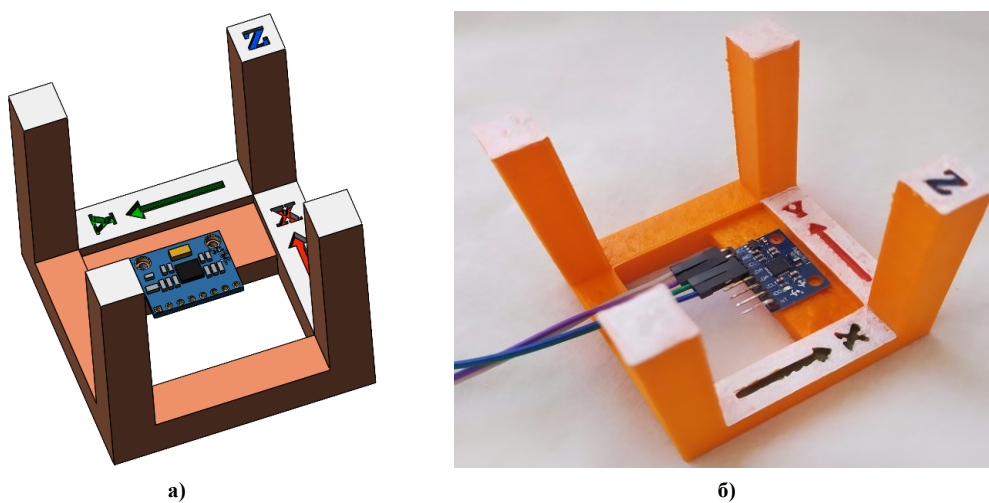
Калібрувальний куб: а) 3D-модель; б) – готовий виріб
